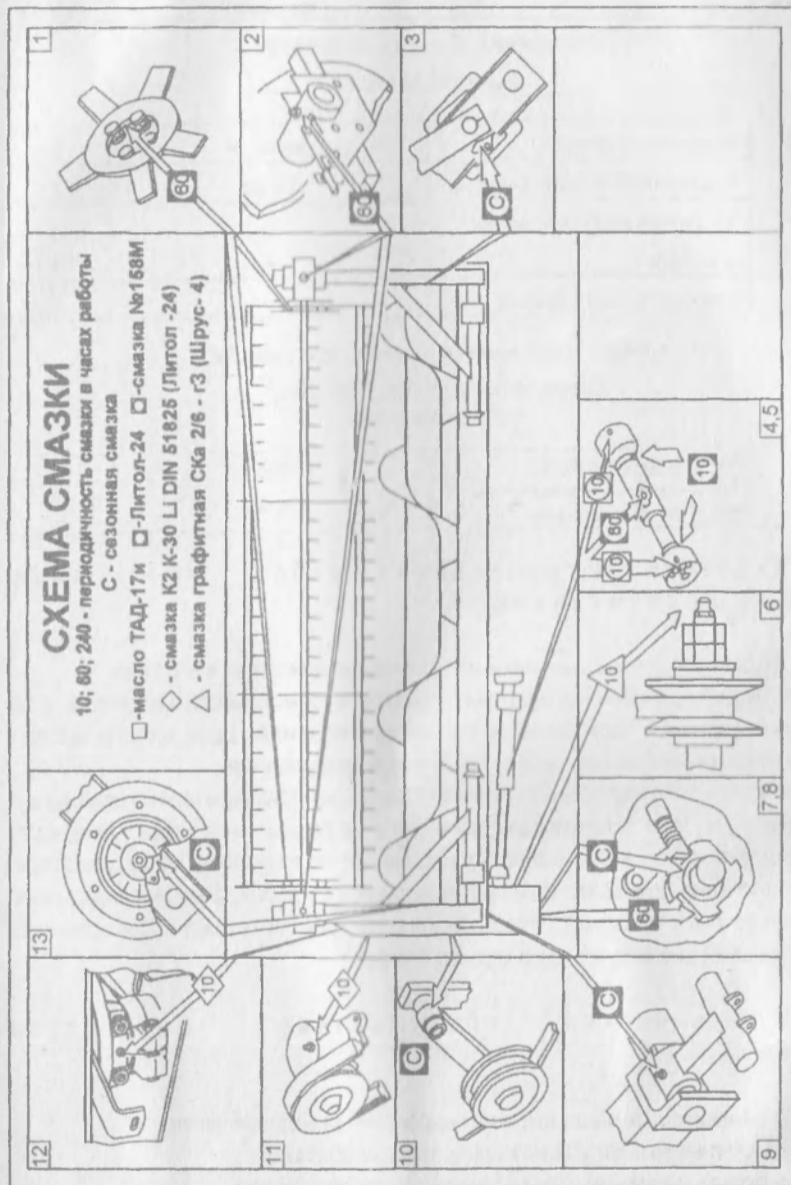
Схема смазки жатки для зерновых культур
